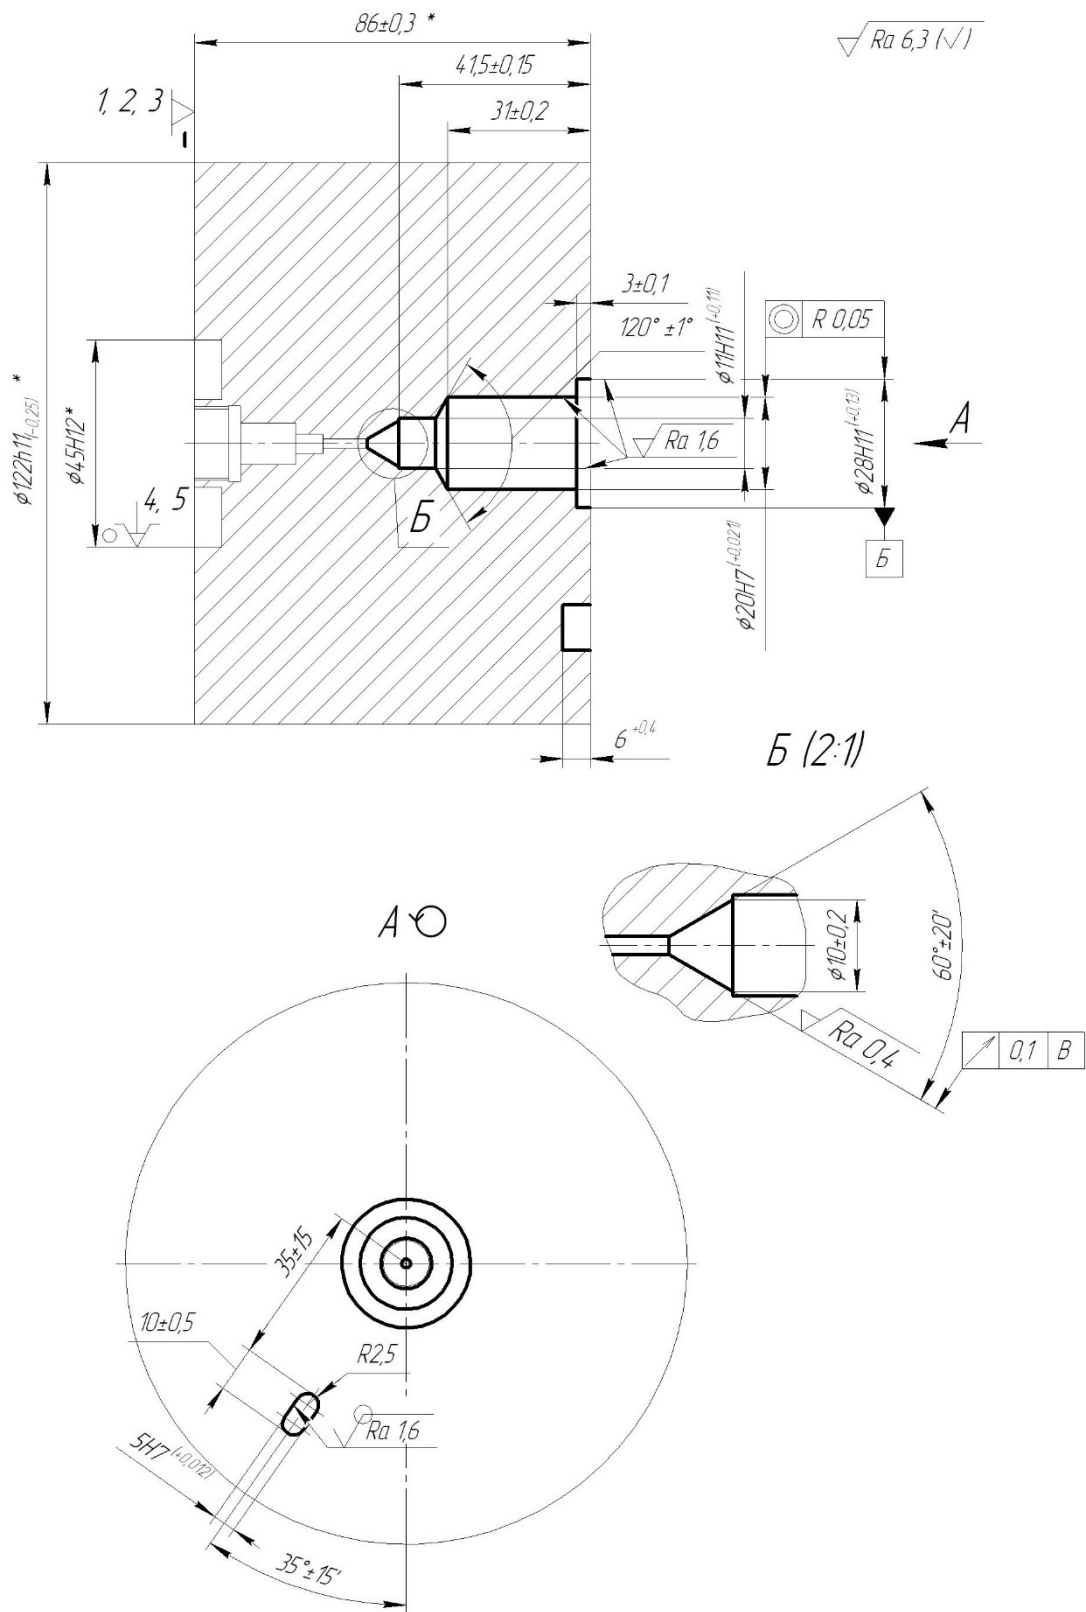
Альтернативна схема базування та закріплення заготовки на операції 035
